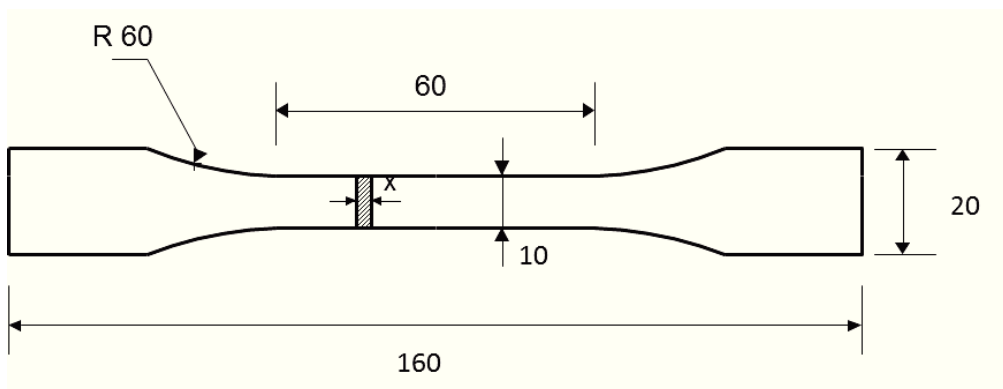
Dimensões de provete com geometria "Osso de Cão" [28]
